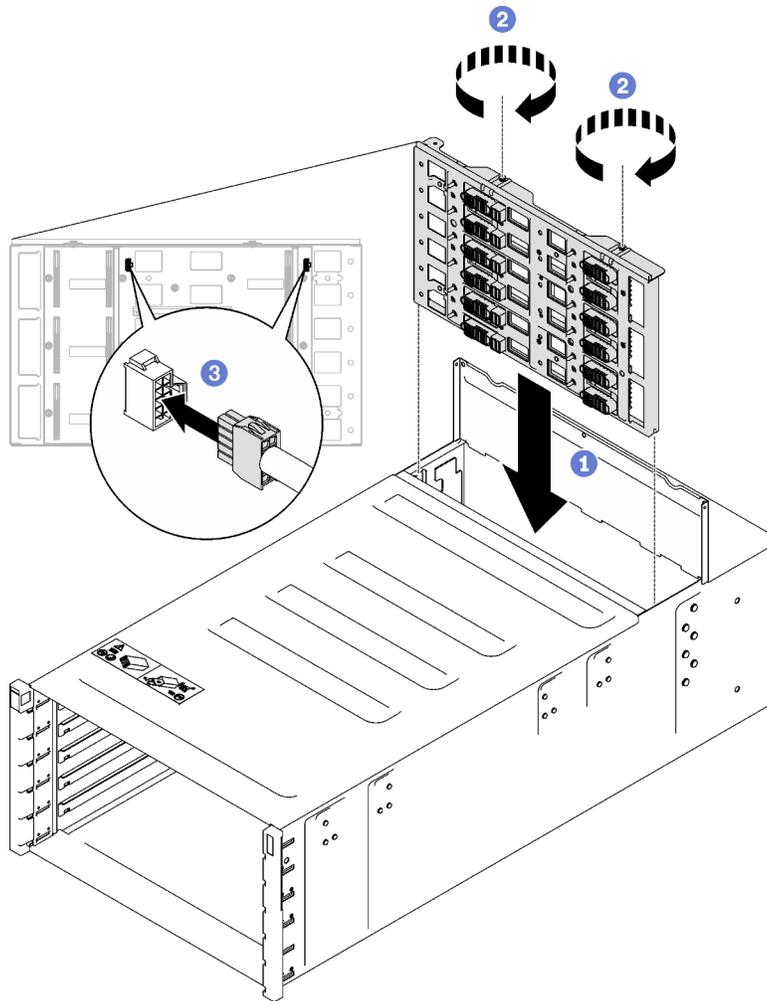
Installieren der Mittelplatte des Gehäuses
